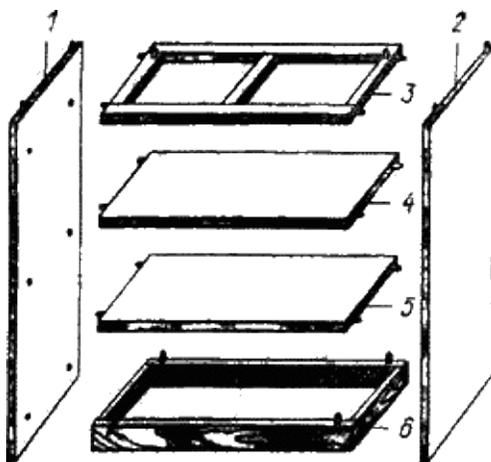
Детали разделочного стола-шкафа со вставными шипами: 1 и 2 — боковые стенки; 3 — подъязычная рамка; 4 — полка; 5 — днище; 6 — цоколь
